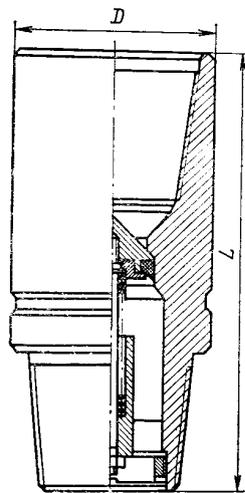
Клапан обратный для бурильных труб конусный с резиновым уплотнителем (КОБ)
